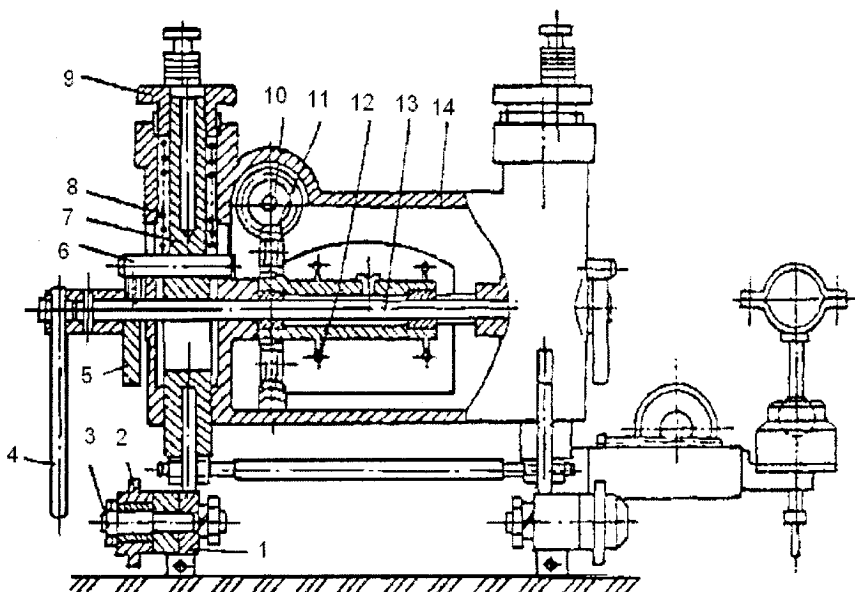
Переносний труборіз ГРВ-2М: 1 — шасі; 2 — колеса; 3 — осі; 4 — ручка; 5 — ексцентрики; 6 — пальці; 7 — штанги; 8 — пружини; 9 — регулювальні гайки; 10 — черв'як; 11 — черв'ячне колесо; 12 — подвоєна зірочка; 13 — вісь; 14 — корпус
